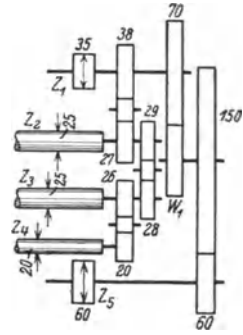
Streckwerk zur Flügelspinnmaschine.
